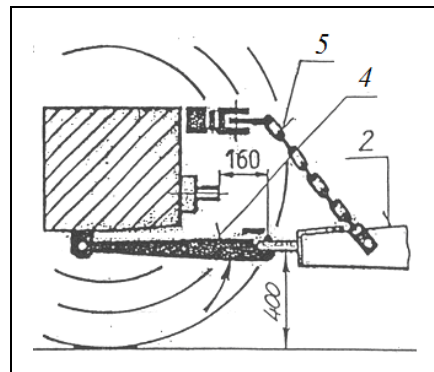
Присоединение пресс-подборщика с нижним сцепным транспортным устройством
